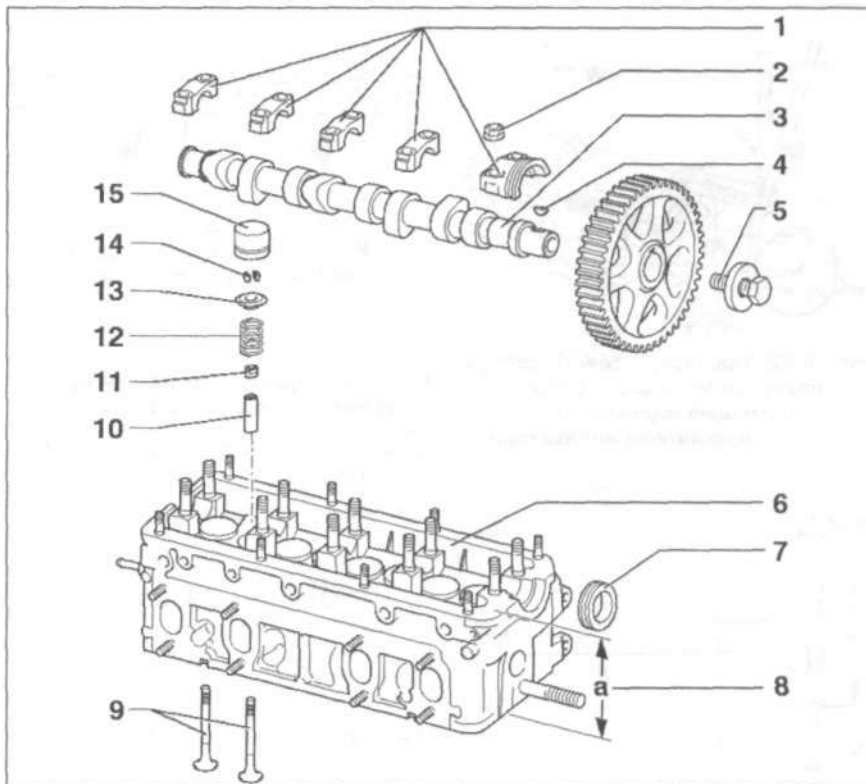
Элементы газораспределительного механизма двигателя AFT:
